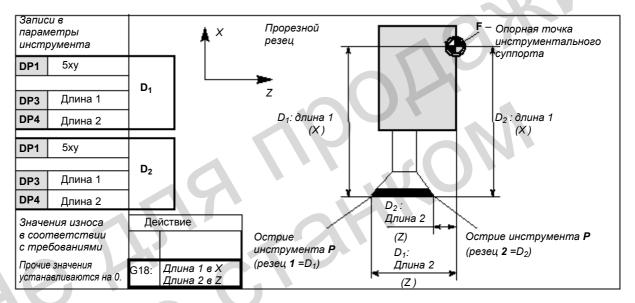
Токарный инструмент в с двумя резцами – коррекция длин
